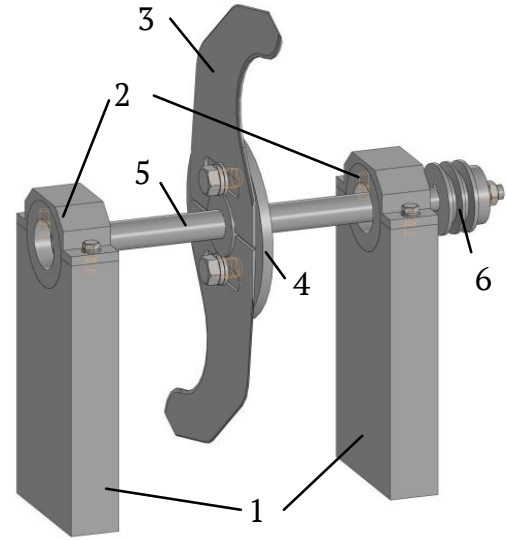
Модель стенда для исследования динамических усилий в приводе ножевого вала куттера: 1 – стойки; 2 – подшипниковые узлы с датчиками давления; 3 – ножи куттера; 4 – фланец крепления ножей; 5 – ножевой вал; 6 – приводной шкив
